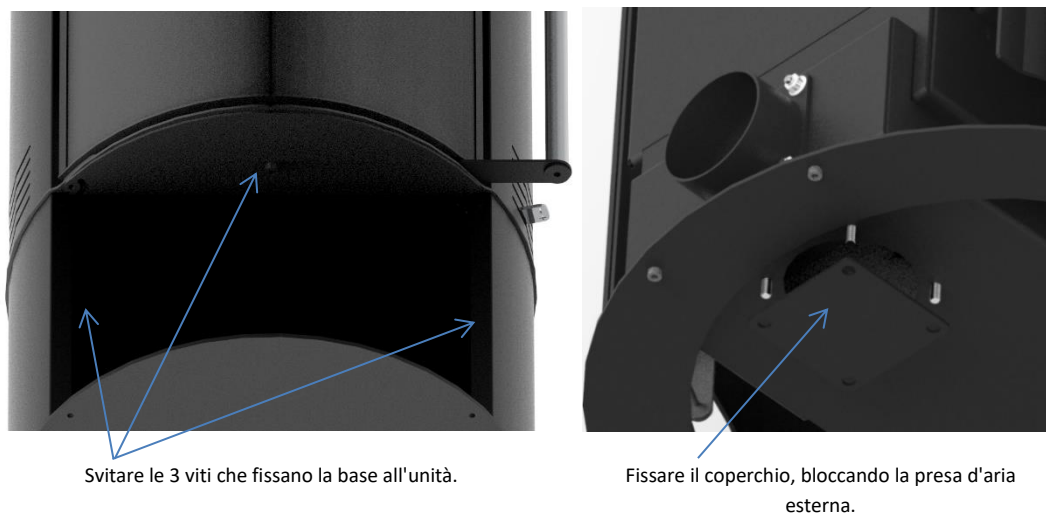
Vista dal basso dell'unità, blocco della presa d'aria esterna sotto l'unità
